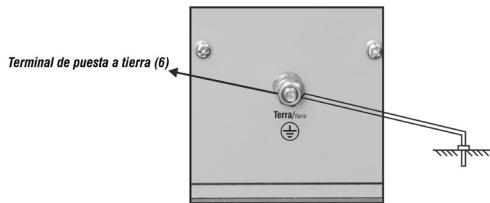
Puesta a tierra del generador de soldadura
